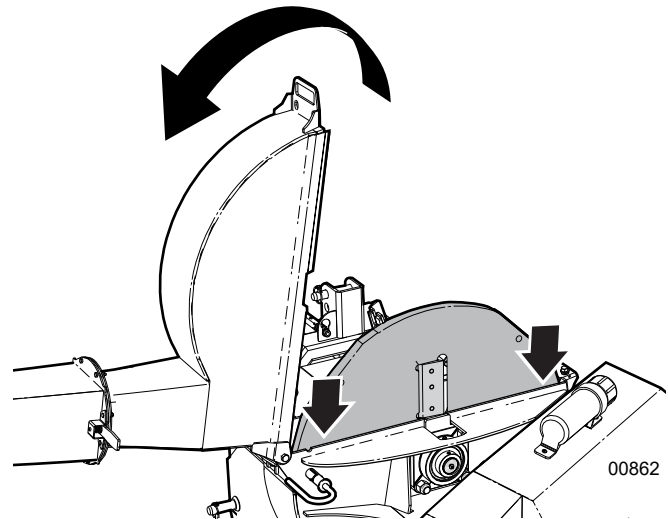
Ouvrez le boîtier supérieur du rotor
